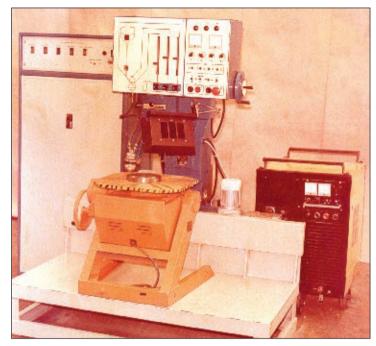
Универсальная установка ОБ 2184 для плазменно-порошковой наплавки
